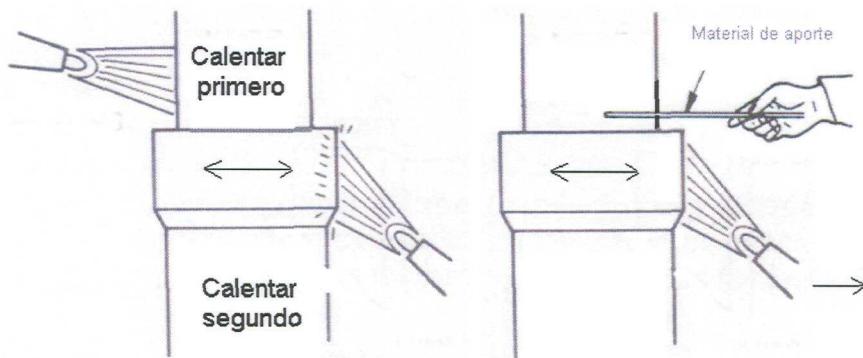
Procedimiento de calentamiento para soldadura de tubería.
